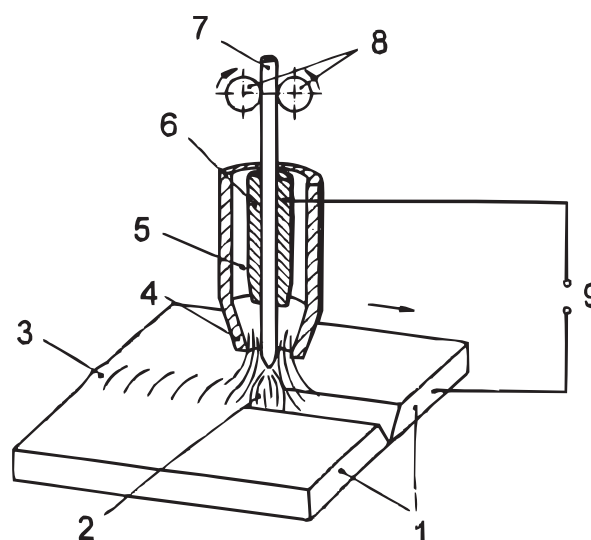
Prinzip des gasgeschützten Metall-Lichtbogenschweißens nach ISO 857-1
